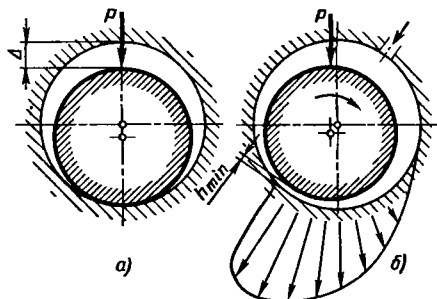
Схема возникновения несущего масляного слоя в подшипнике
